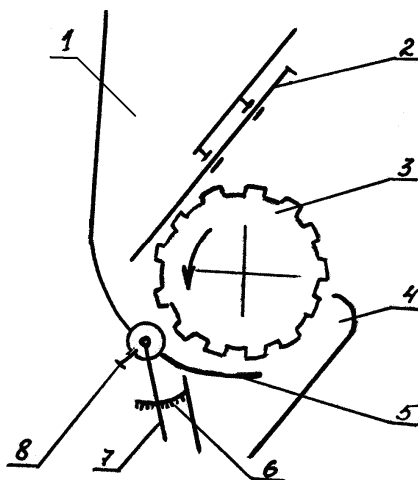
Схема катушечно-штифтового туковывсевающего аппарата: 1 – ящик; 2 – задвижка; 3 – катушка штифтовая; 4 – корпус; 5 – клапан (дно); 6 – сектор; 7 – рычаг; 8 – стопорный болт
